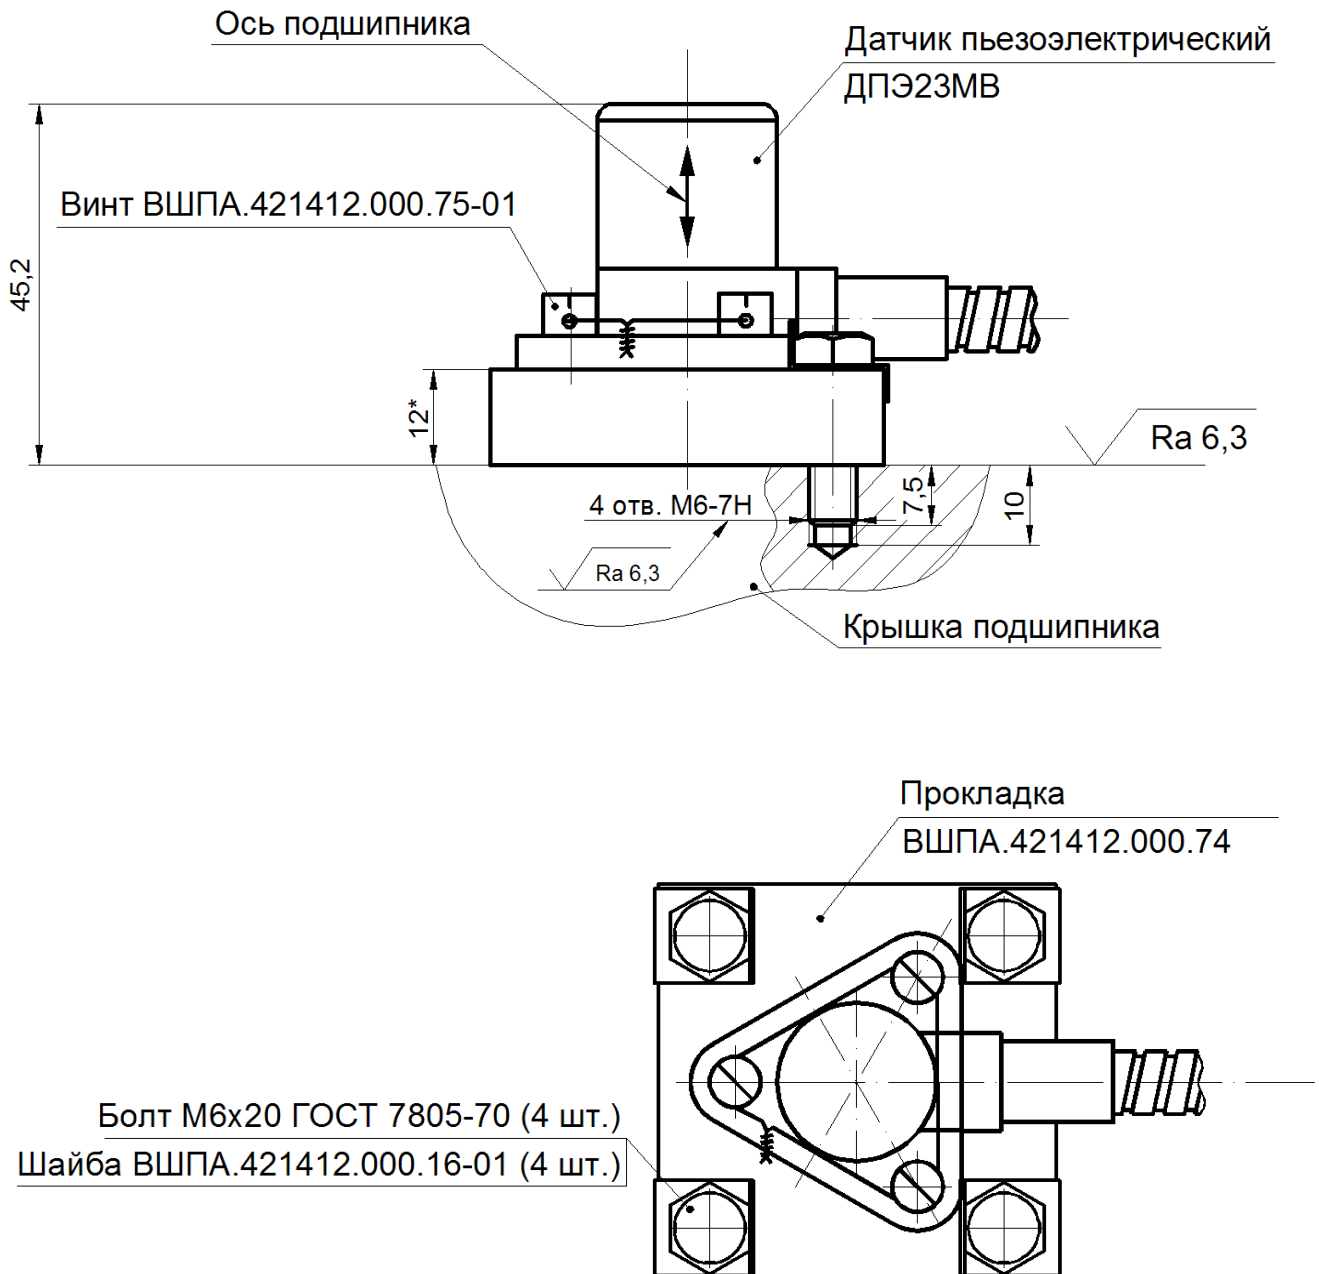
Установка датчика пьезоэлектрического ДПЭ23МВ на крышке подшипника
